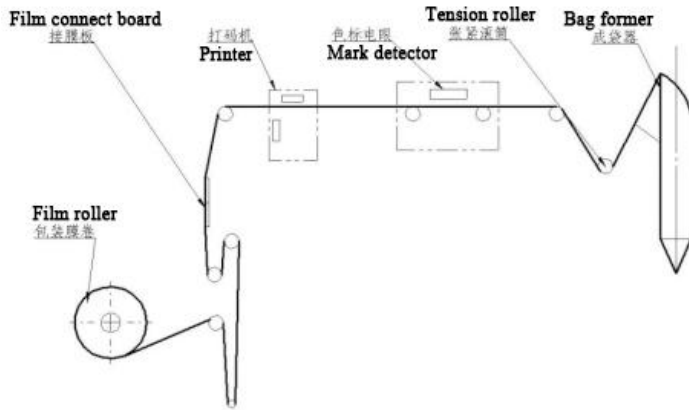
走膜成袋示意图 FIG. 28 schematic diagram of film transfer into bag
